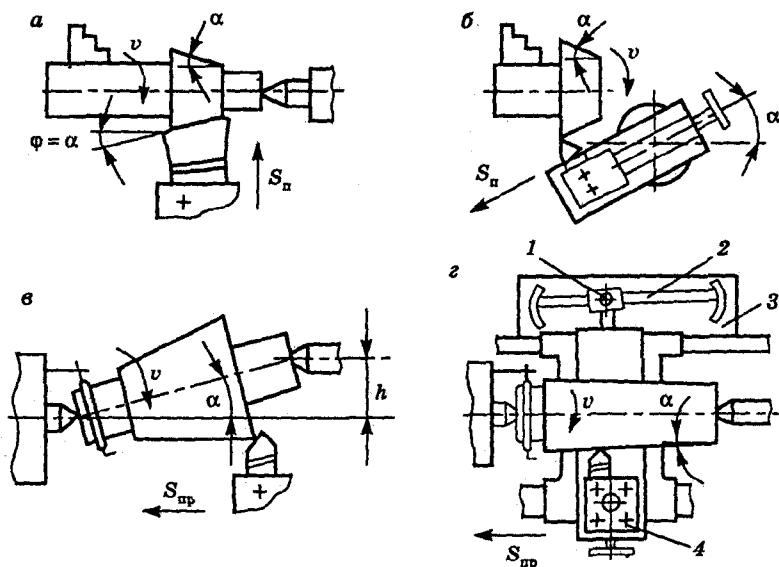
Схемы обтачивания наружных конических поверхностей на токарно-винторезном станке:
